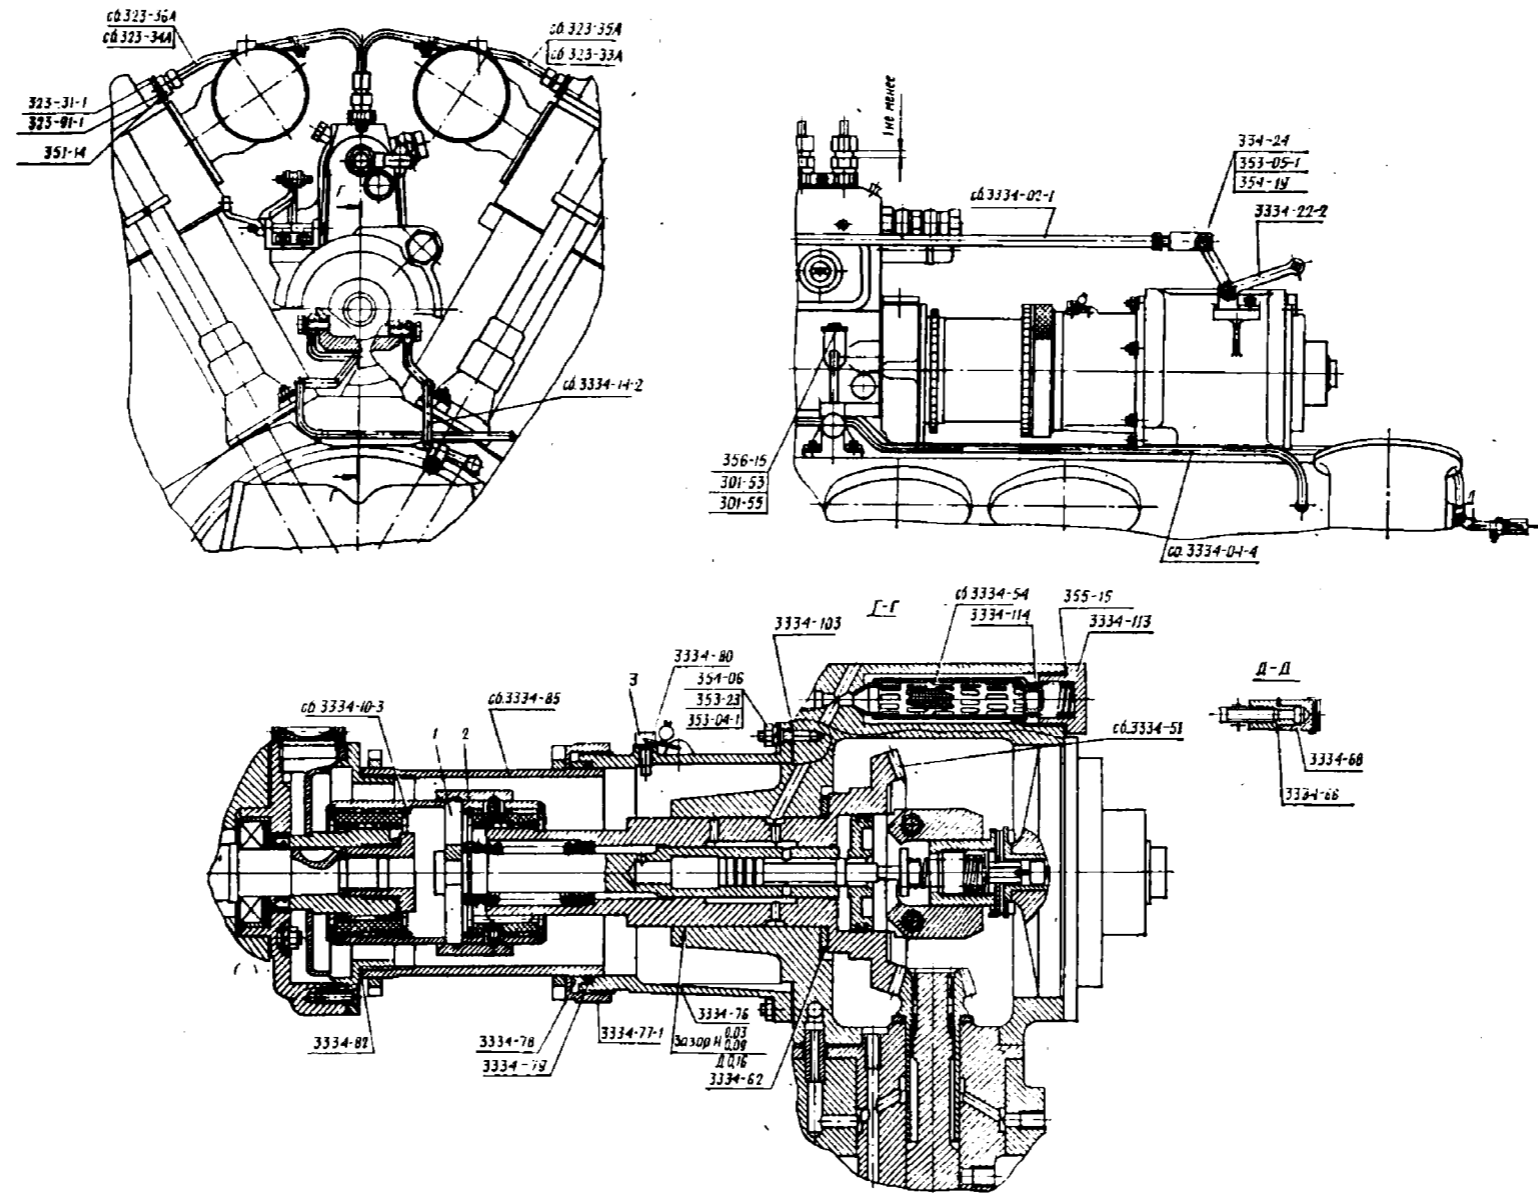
Установка топливного насоса, трубок высокого давления и автомата опережения сб.3334-00-6:
